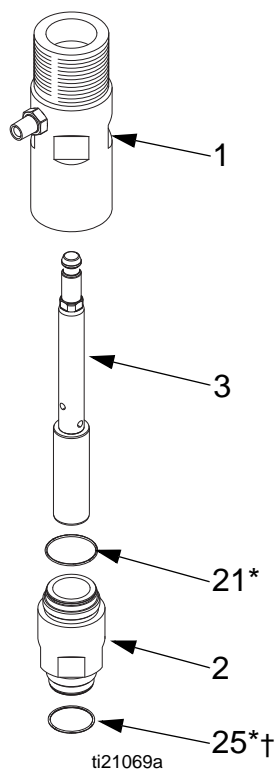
Assemblez l'ensemble piston/tige et les cylindres.
